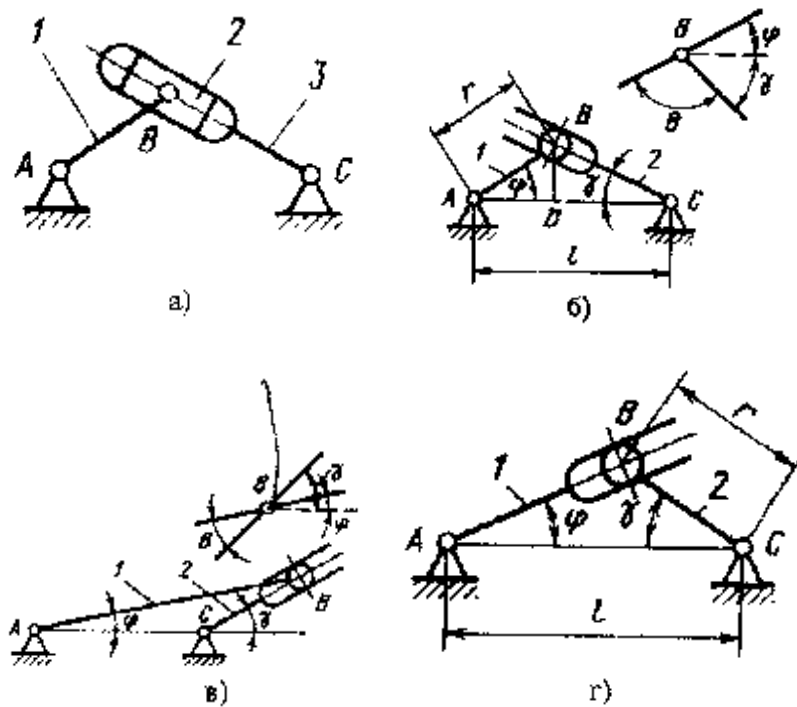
Конструктивні різновиди кулісного механізму
